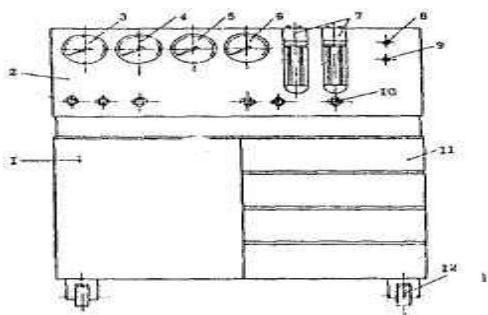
Установка передвижная для проверки газовой аппаратуры
